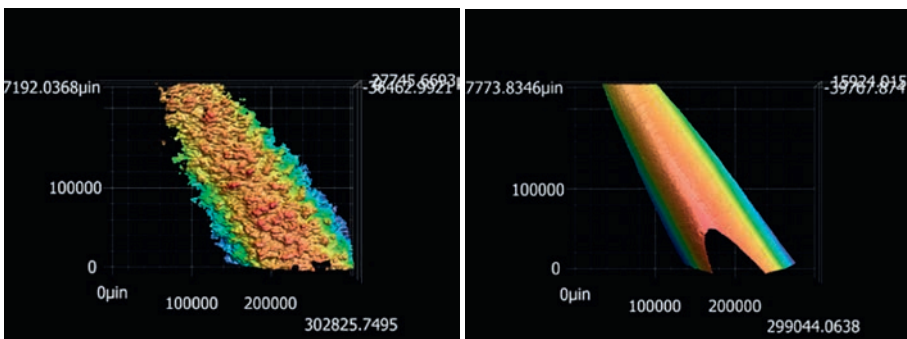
Шероховатость поверхности входной кромки лопатки после СЭЛП (а) и прецизионной ЭХО (б)
